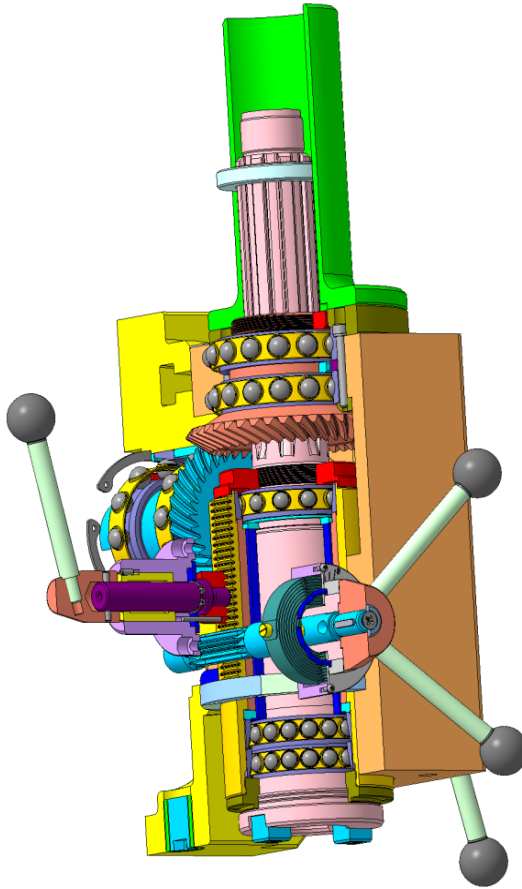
3D-модель вертикальної шпindelної голівки
